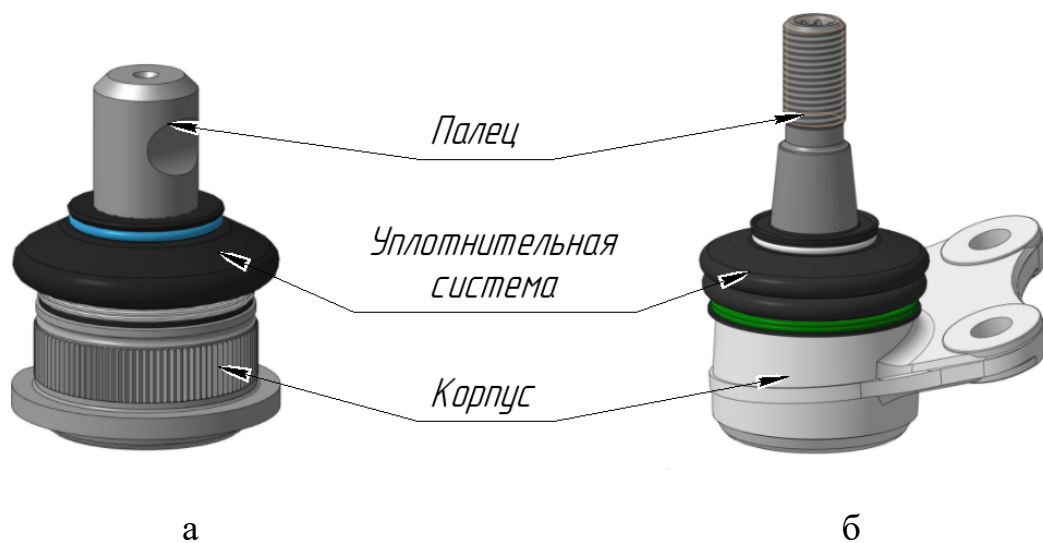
Основные типы крепления шарового пальца к ответной детали: а – с фиксацией цилиндрического участка клеммой ответной детали; б – с конусной посадкой и фиксацией резьбы пальца гайкой
